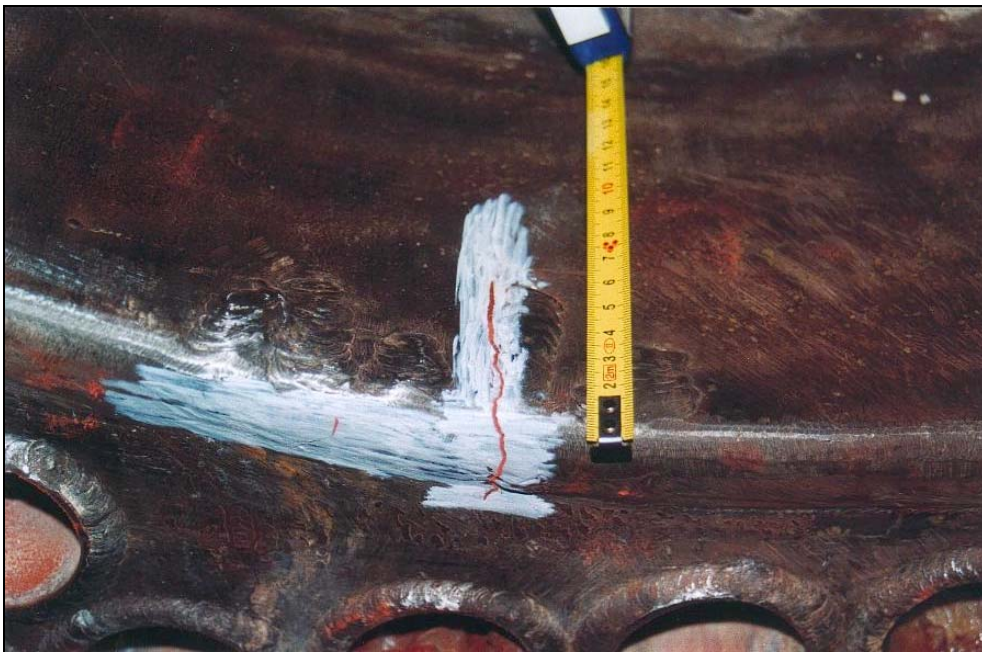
Extremo del fogón sobresaliendo de la placa tubular caliente (grietas detectadas con partículas magnéticas).
